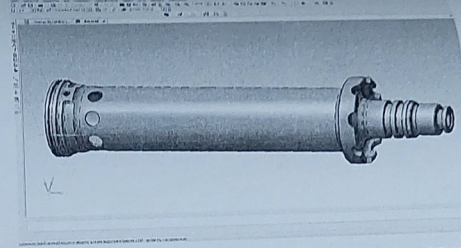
Твердотільна модель "Циліндр" в SOLIDWORKS
